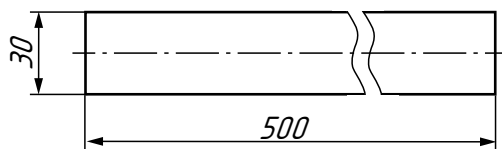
Чертёж детали из древесины (изображение линии обрыва на виде спереди)
